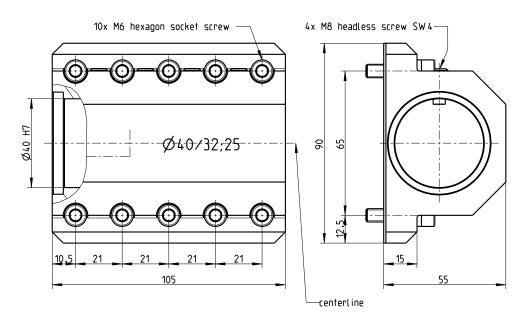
Werkzeughalter passend zu Sandvik Coroturn SL mit 40 mm Durchmesser, Typ 9129AG40
